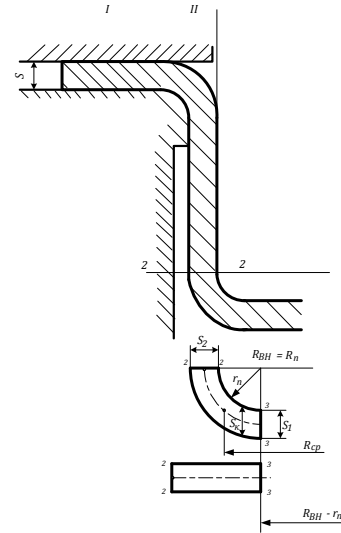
Схема штампування-витяжки циліндричного стаканчика для визначення тимчасового опору наклепаного металу
